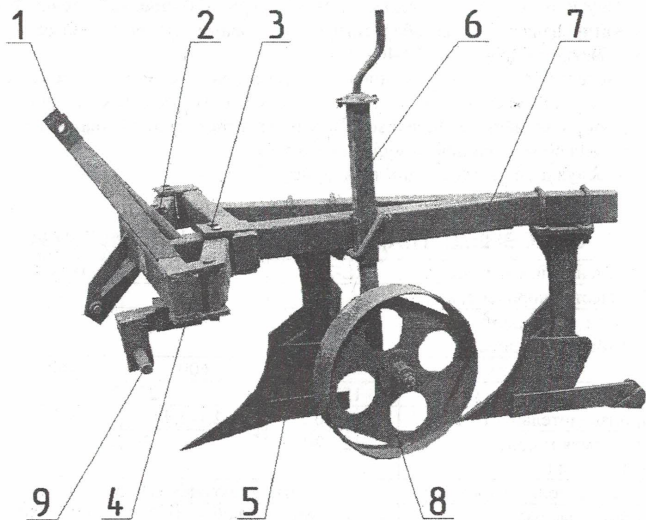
Устройство плуга двухкорпусного тип 1L-220
